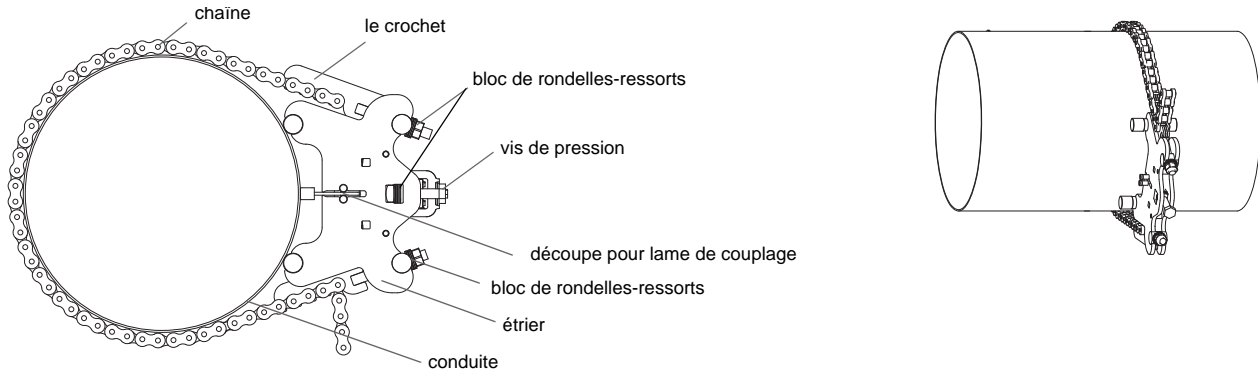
Le dispositif de fixation à la conduite sur la conduite (vue de l'avant)
